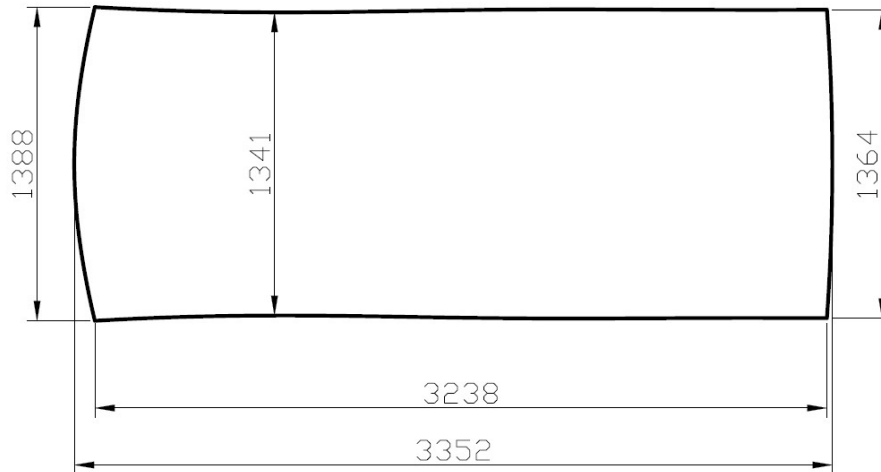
Dimensiones del techo. Cotas expresadas en milímetros.
